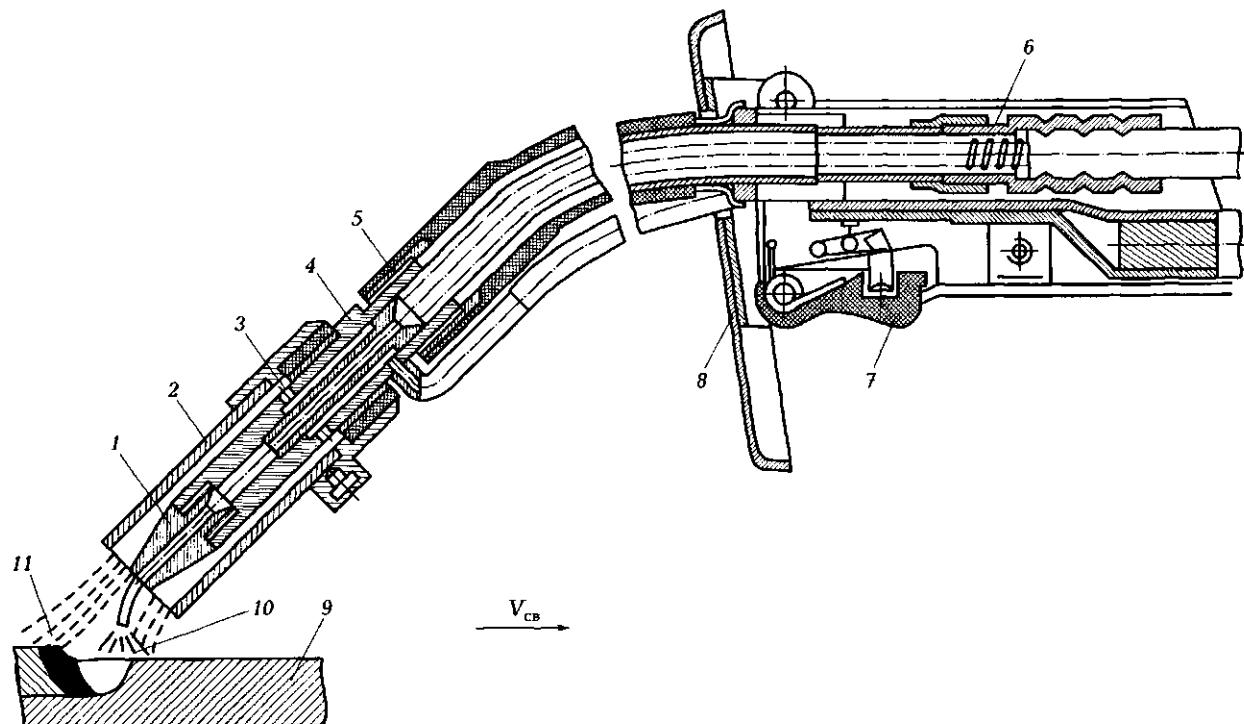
Конструкция сварочной горелки серии ГДПГ для сварки плавящимся электродом в защитных газах:
